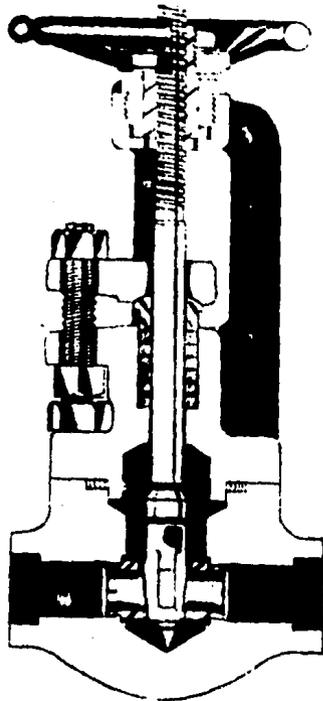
Válvula de compuerta de cuña sencilla, con extremos soldables a profundidad.
